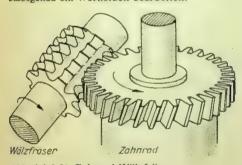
Zahnrad-Wälzfräsen
